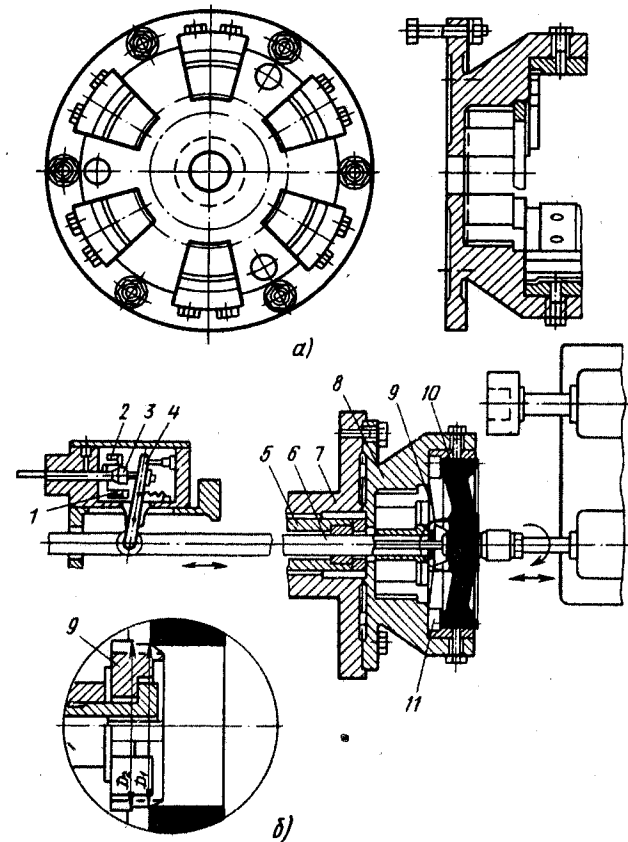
Мембранный патрон (а) и схема шлифования отверстия и торца зубчатого колеса в мембранном патроне (б): 1, 2 — микровыключатели, 3, 5, 6 — штоки, 4 — рычаг электроконтактной головки; 7 — патрон, 8 — мембранный диск, 9 — калибр, 10 — заготовка, 11 — кулачки
